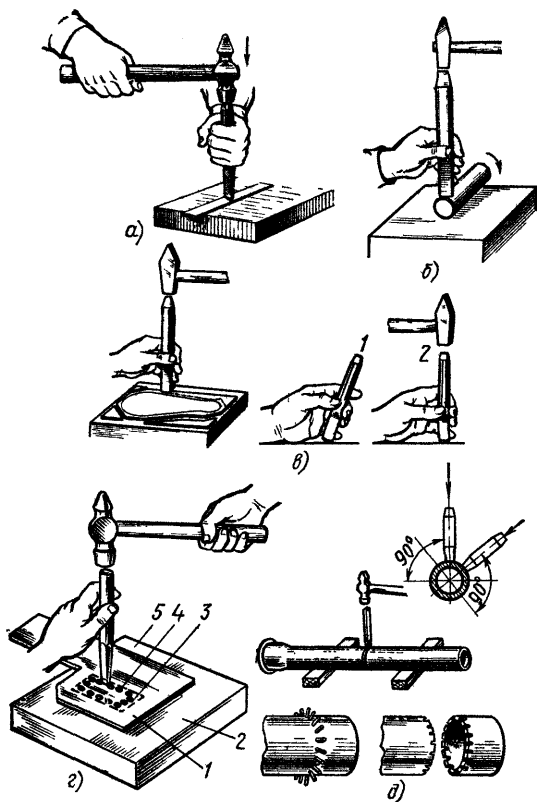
Разрубание и вырубание металлов: а — рубка полосового металла, б — рубка круглого металла, в — прорубание контура и установка зубила при рубке листового металла: 1 — наклонно, 2 — вертикально; г — рубка толстого листового металла, д — рубка труб на деревянных подкладках
